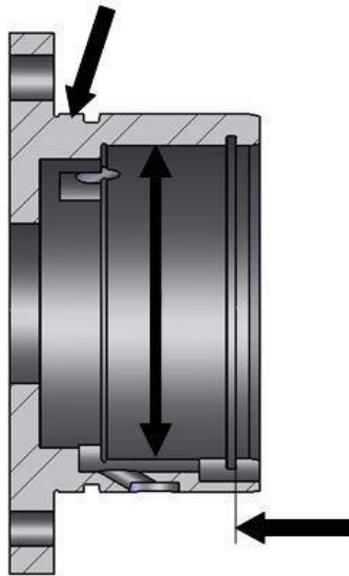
Áreas de inspección – Grupo 1 y 2 de la caja de rodamientos
